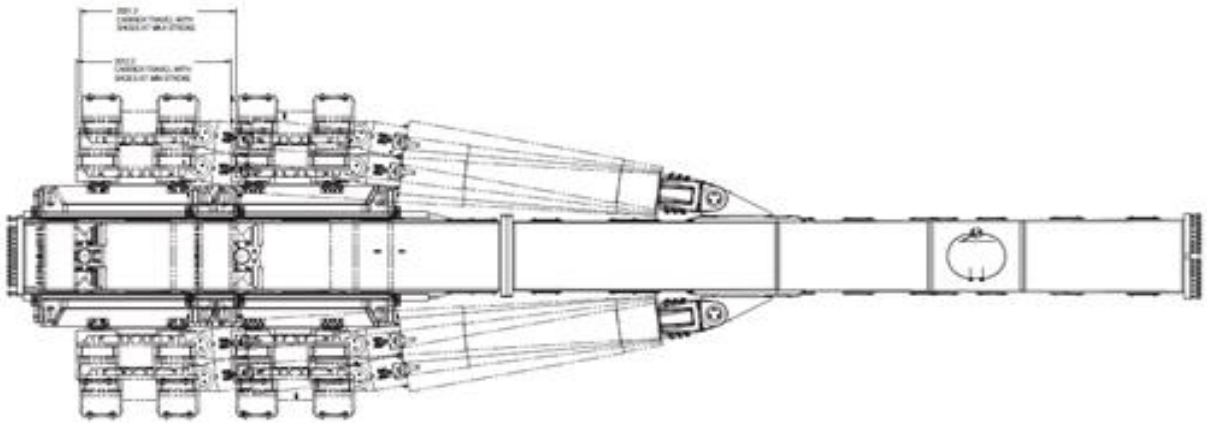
Conjunto de Zapatas, vista planta, TBM Robbins MB139-396 (The Robbins Company, 2014)
